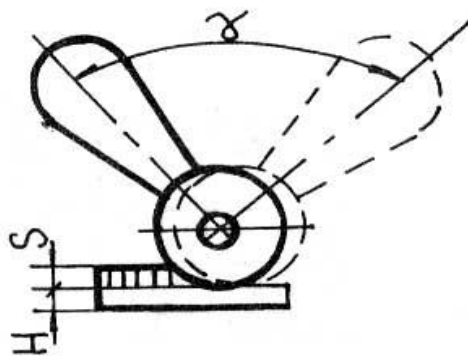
Круговой эксцентрик для зажима заготовки по размеру H
